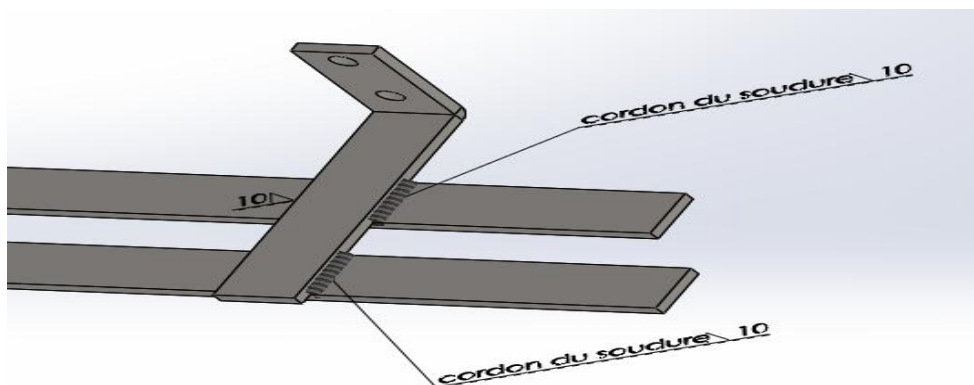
Dessin solidworks (soudure des fer-plats).
